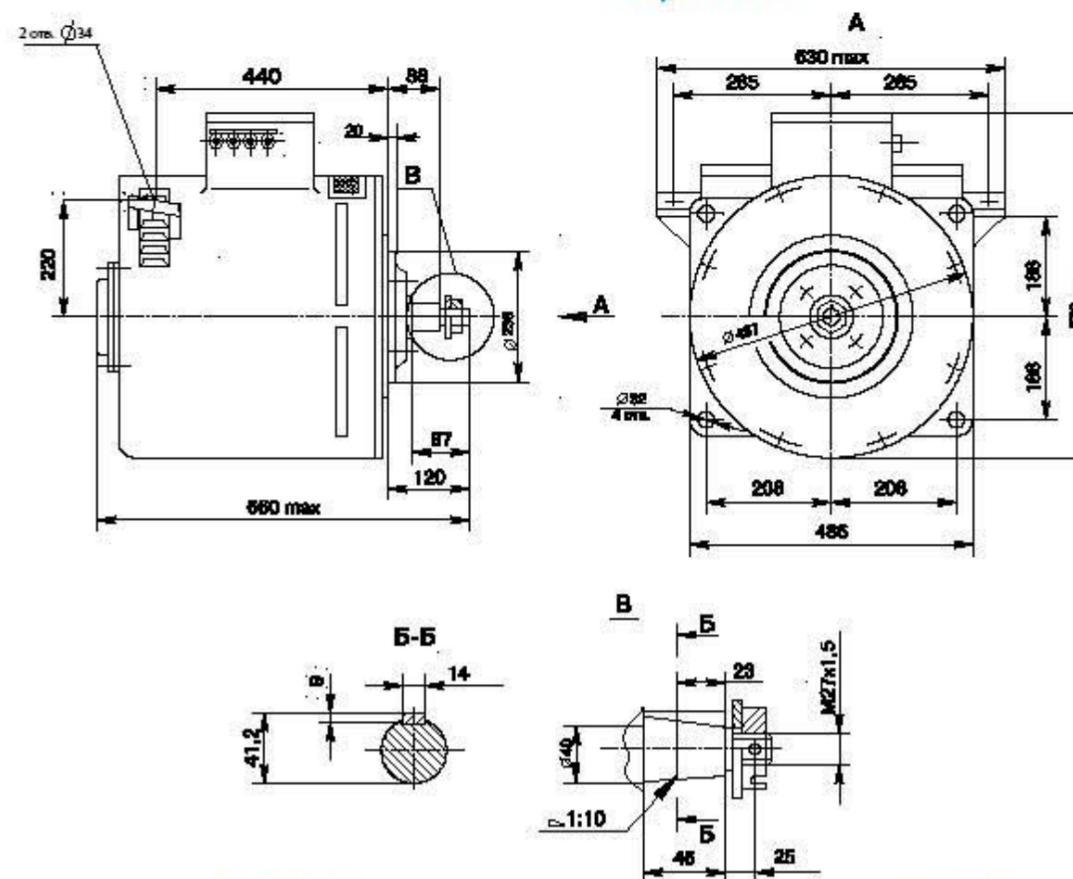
Габаритные и установочные размеры электродвигателя ДТН-12/7
